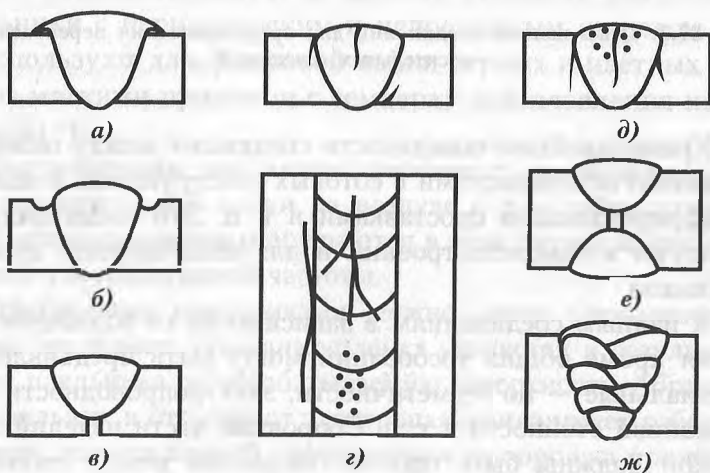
Виды дефектов в сварных соединениях
